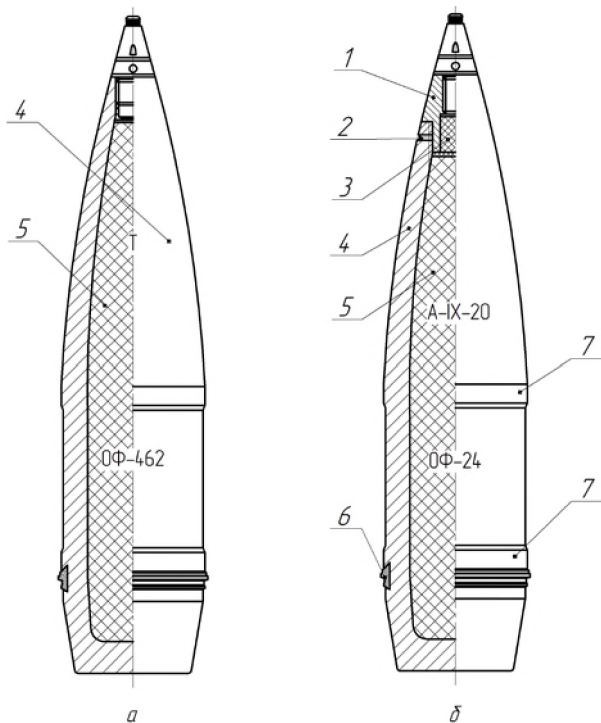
Конструкции снарядов: а – цельнокорпусная; б – с переходной втулкой; 1 – переходная втулка; 2 – стопорный винт; 3 – дополнительный детонатор; 4 – корпус; 5 – разрывной заряд; 6 – ведущий поясик; 7 – центрующие утолщения
